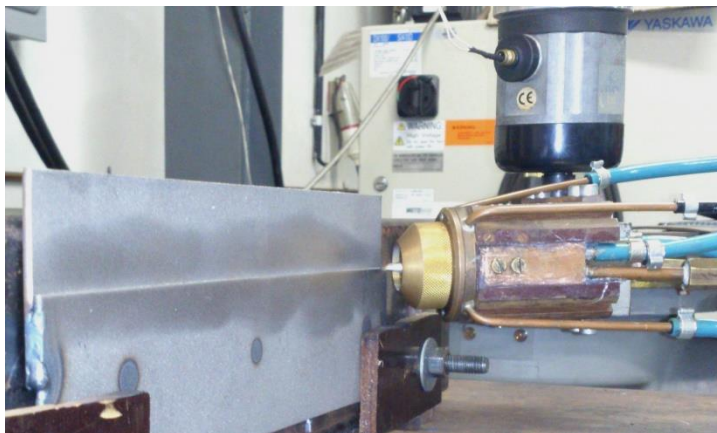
Soldagem de chapas em junta sobreposta na posição horizontal
